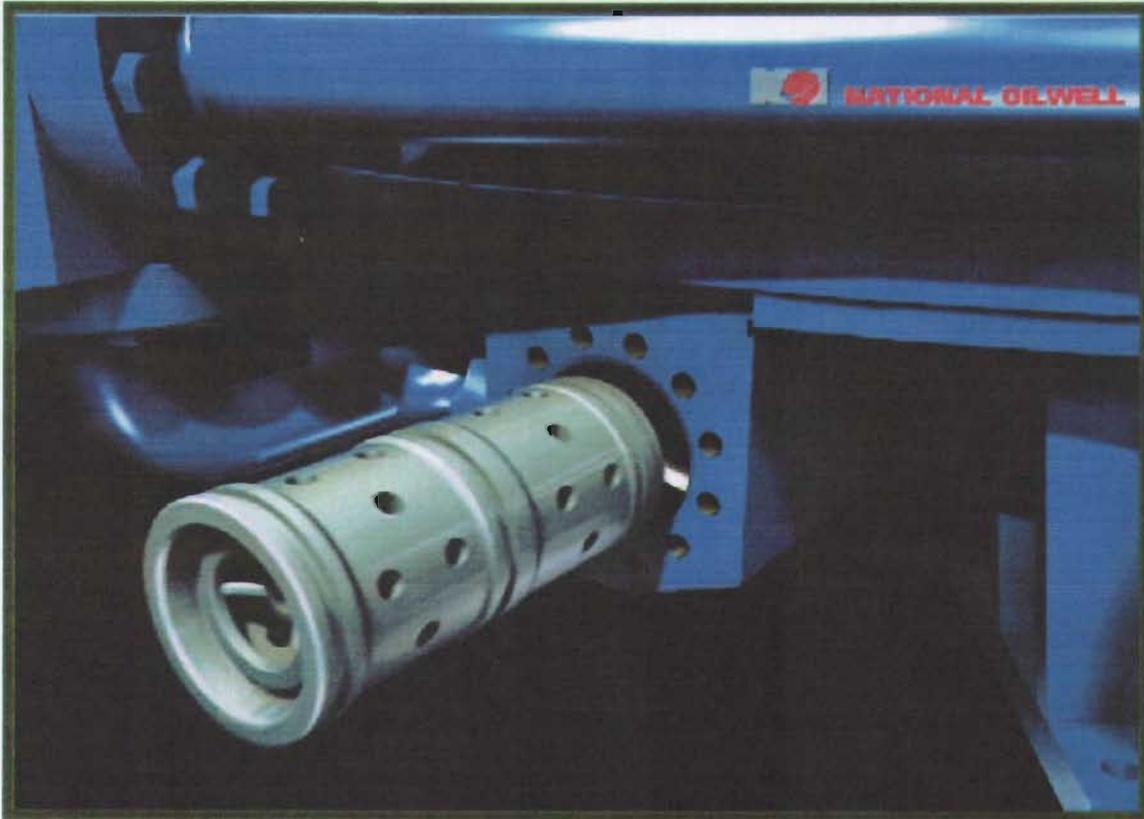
VISTA DEL EXTREMO HIDRAULICO
